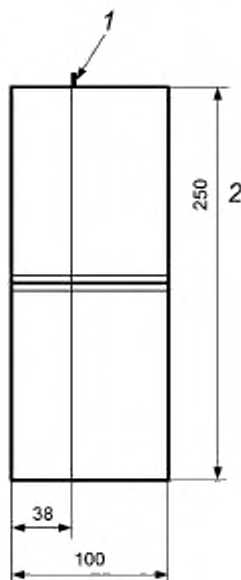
Лабораторная проба со швами и разметкой образцов для испытания
